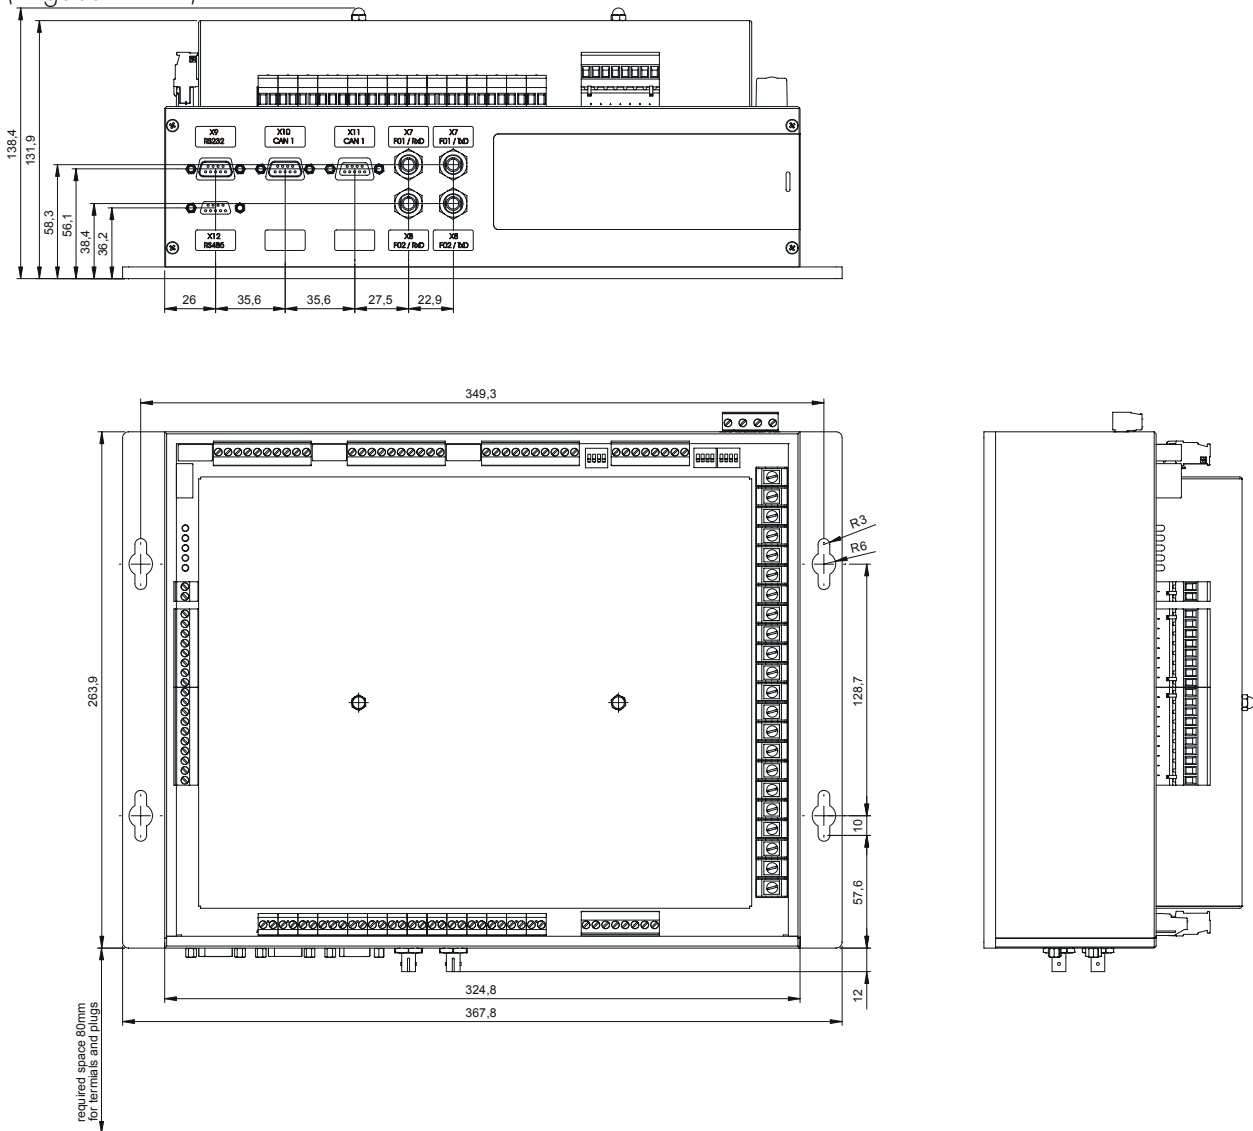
Gehäuseabmessungen des CSP2-T25
